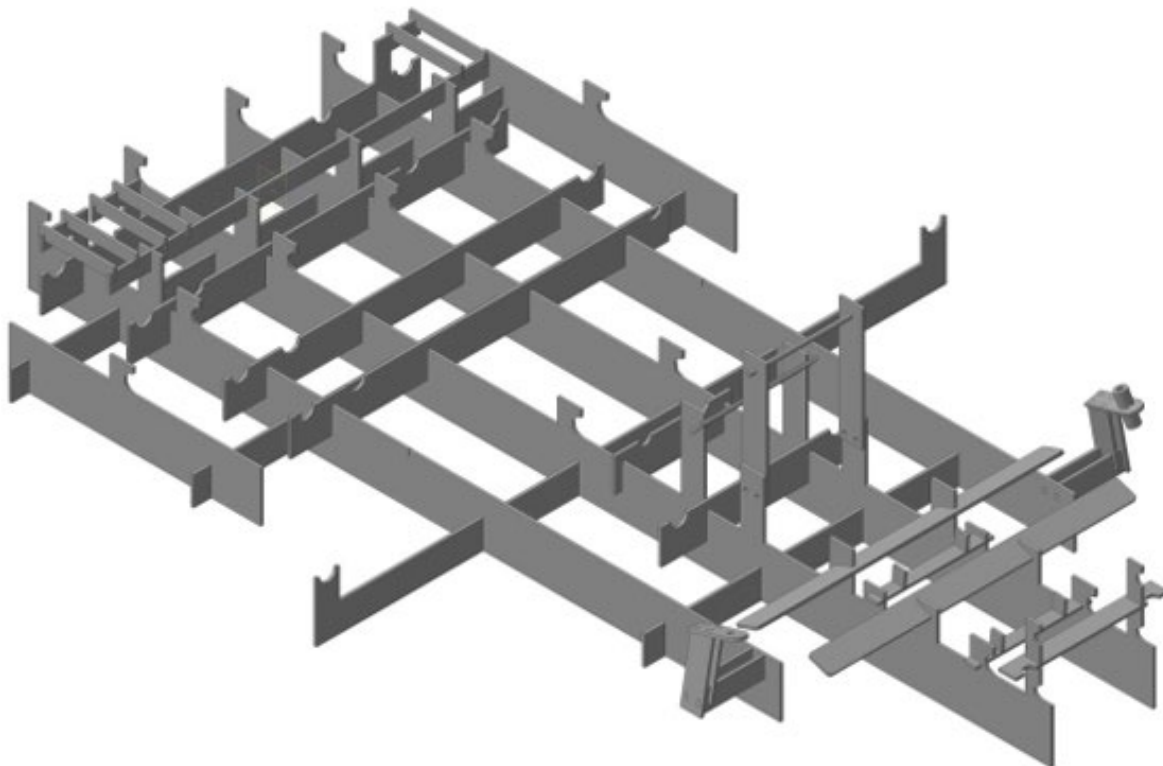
Кондуктор для точной сварки пространственной рамы спортивного карта
